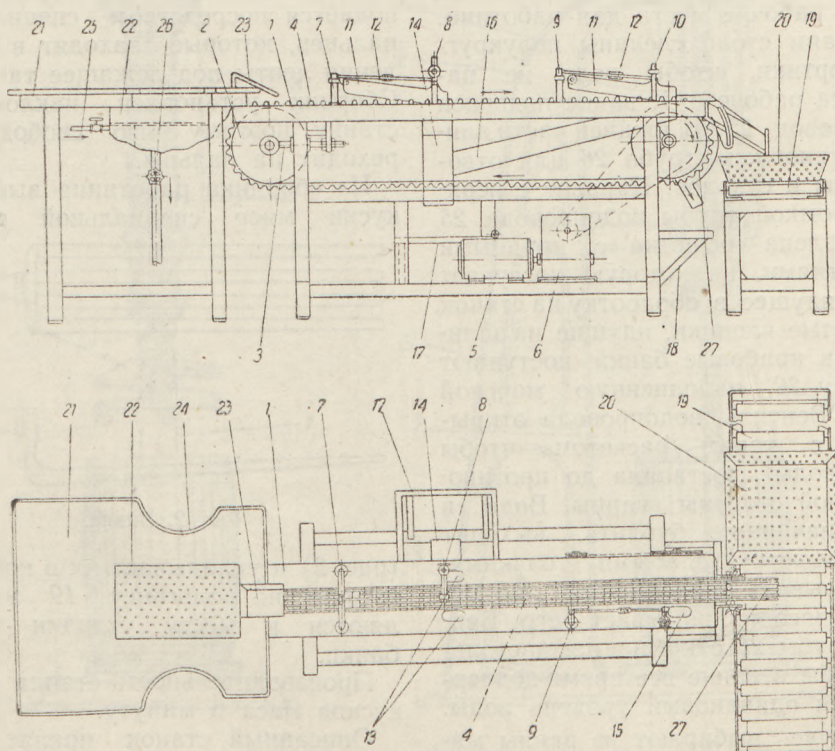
Схема станка конструкции С. Е. Губаря для резки крабового мяса.
